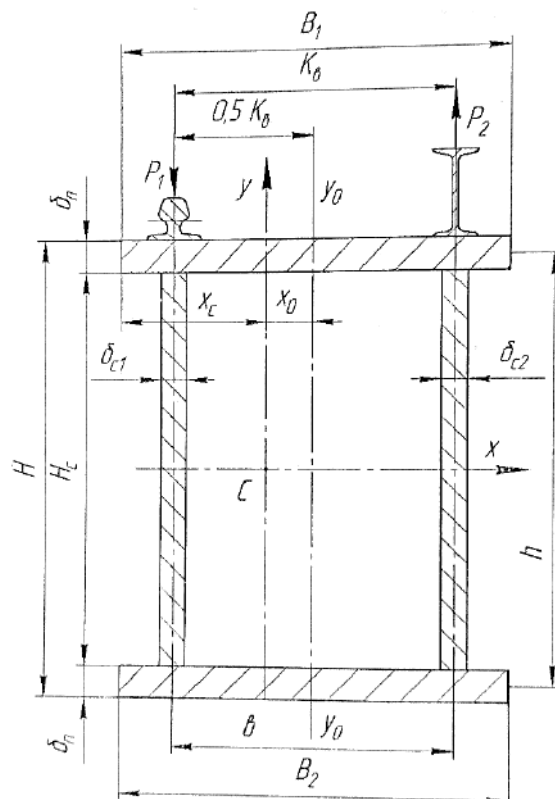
Поперечний перетин головної балки крана з консольним візком
